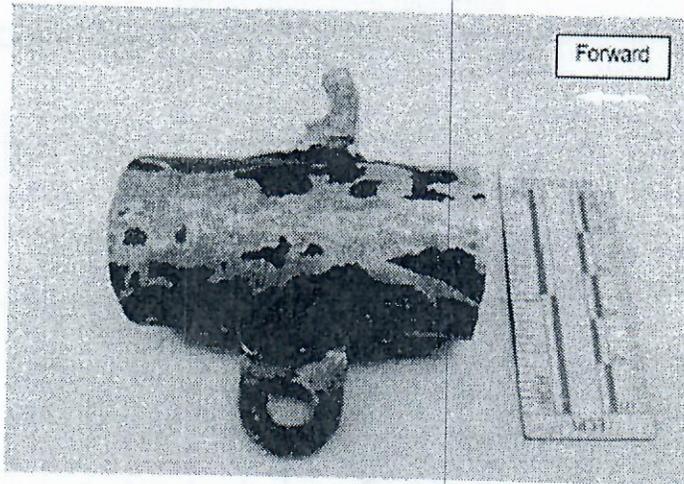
Vista cercana de la sección del tubo estabilizador donde se encuentran las orejas de retención de los cables.
